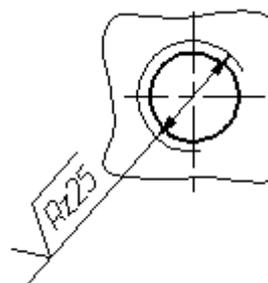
Пример обозначения шероховатости внутренней резьбы
